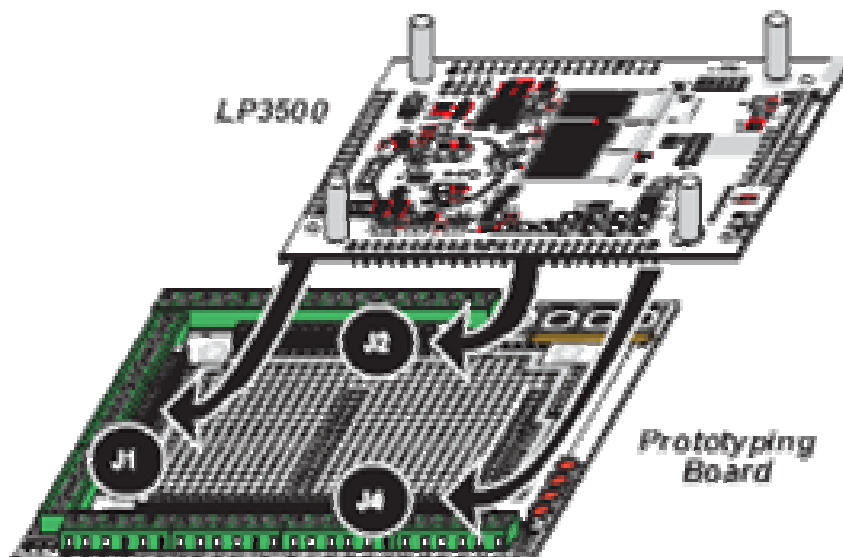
Acoplagem da LP3500 com a placa de prototipagem
